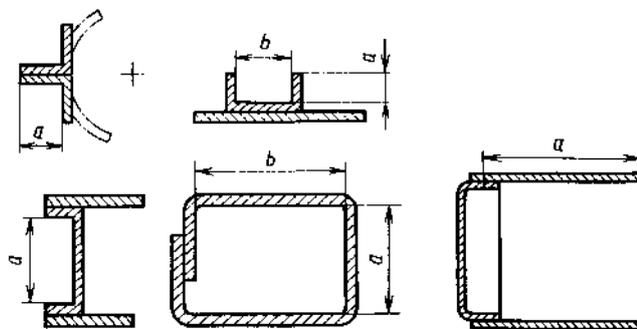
Элементы конструкций, соединенные контактной сваркой
